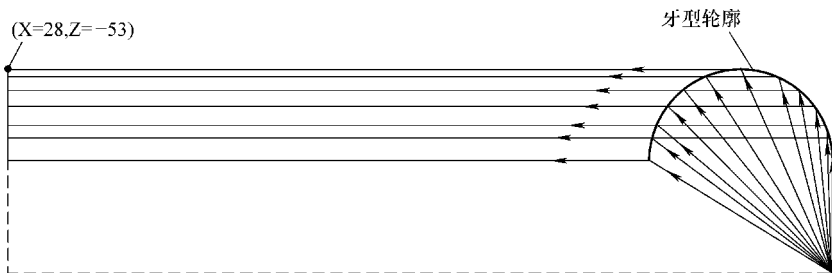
精加工进刀刀具路径示意图（前置刀架）
